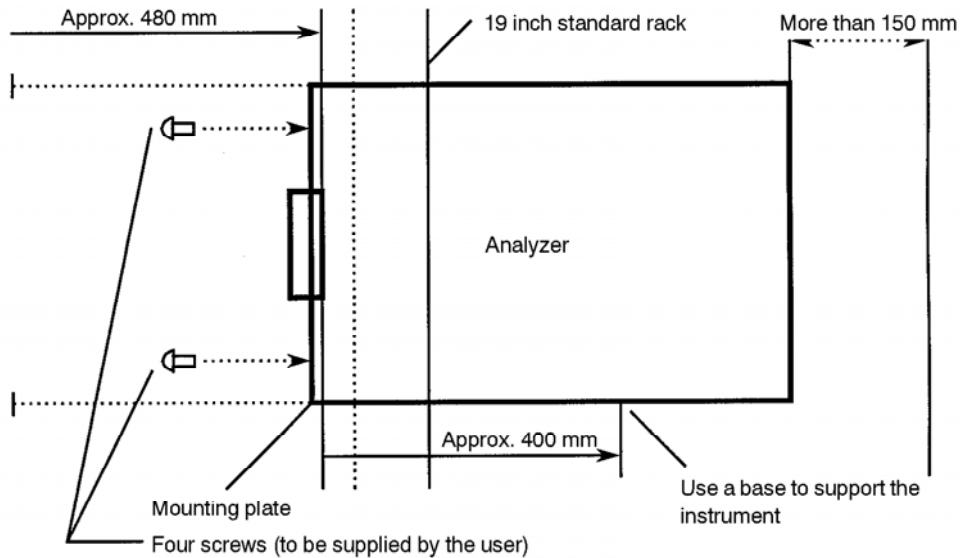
Einbau des APSA-370 in einem 19"-Schrank
